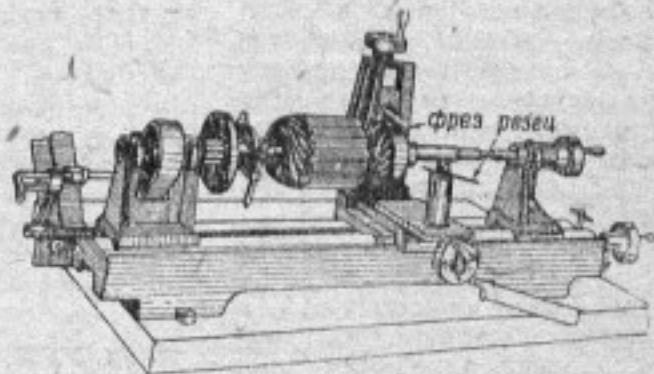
Универсальный станок для фрезеровки и проточки якорей
